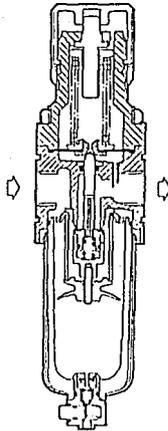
FILTRO REGULADOR COMBINADO EN UN SOLO CUERPO.
